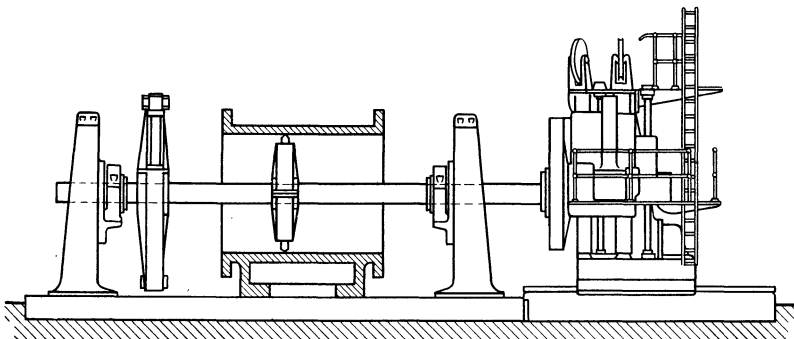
Ausbohrmaschine mit in der Höhe einstellbarem Spindelkasten und verschiebbarem Ständer.
